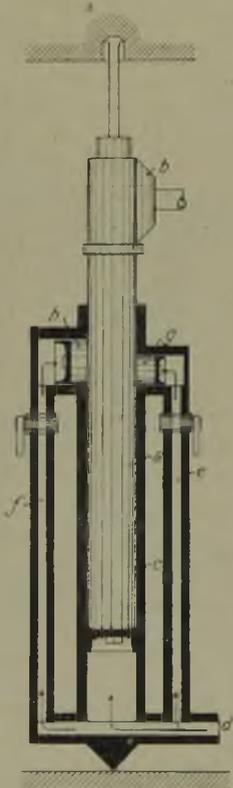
Vorschubregelung der Bohrmaschinenfabrik Glückauf.
